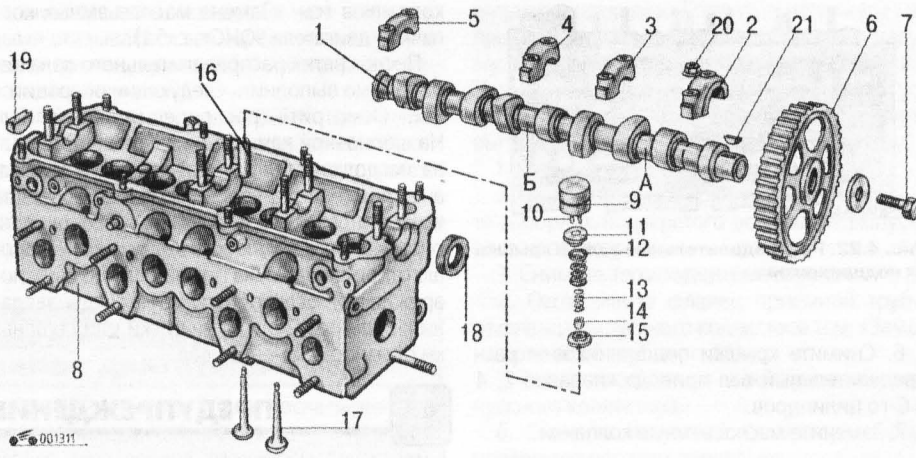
Головка блока цилиндров двигателя SOHC и механизм привода клапанов: 1 – распределительный вал; 2, 3, 4, 5 – крышки подшипников распределительного вала; 6 – зубчатый шкив распределительного вала; 7 – болт крепления зубчатого шкива распределительного вала; 8 – головка блока цилиндров; 9 – гидравлический толкатель; 10 – сухари клапана; 11 – тарелка пружин клапана; 12 – наружная пружина клапана; 13 – внутренняя пружина клапана; 14 – маслосъемный колпачок; 15 – нижняя тарелка пружин клапана; 16 – направляющая втулка клапана; 17 – клапан; 18 – сальник распределительного вала; 19 – заглушка; 20 – гайка крепления крышки подшипника; 21 – сегментная шпонка; А – место нанесения буквенной маркировки распределительного вала; Б – место нанесения цифровой маркировки распределительного вала
